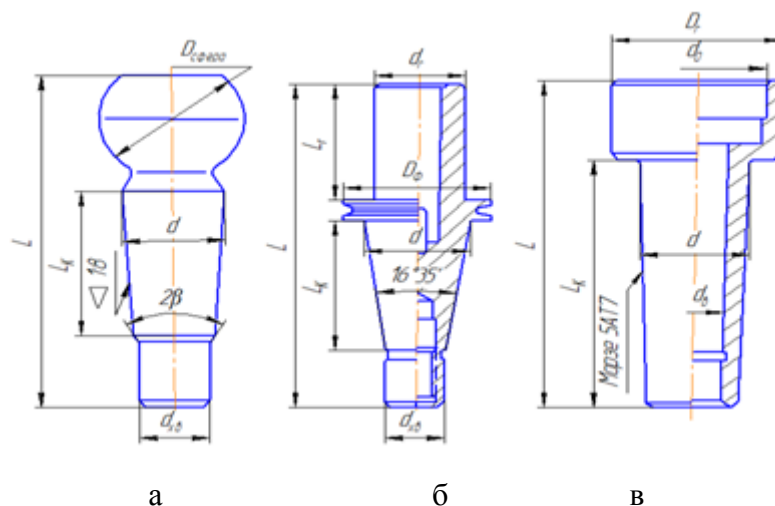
Конструкция типовых деталей с коническими элементами: а – шаровой палец; б – втулка переходная к станкам с числовым программным управлением; в – корпус вращающегося центра
